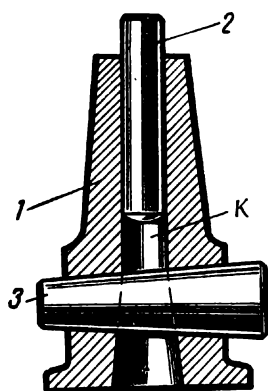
Приспособление для прессования свинцовых опилок:
